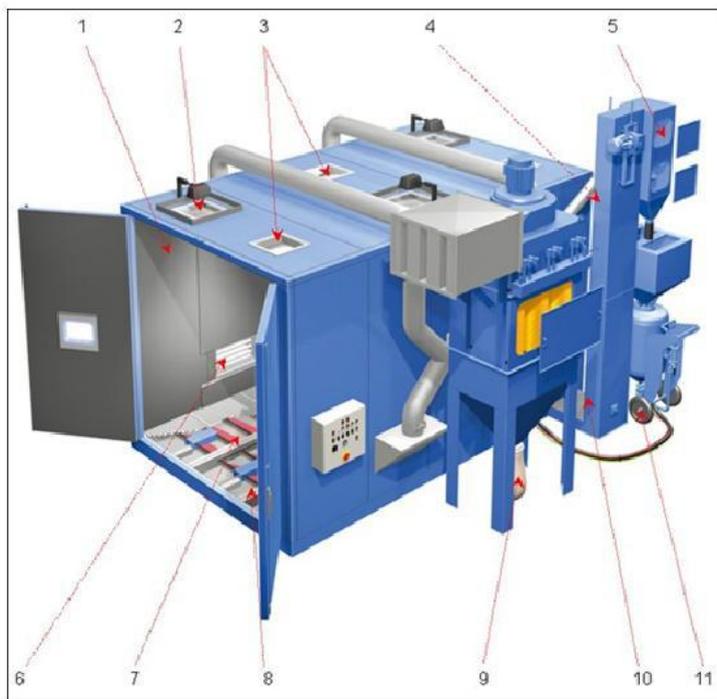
Схема дробеструйной камеры с системой сбора дробы
